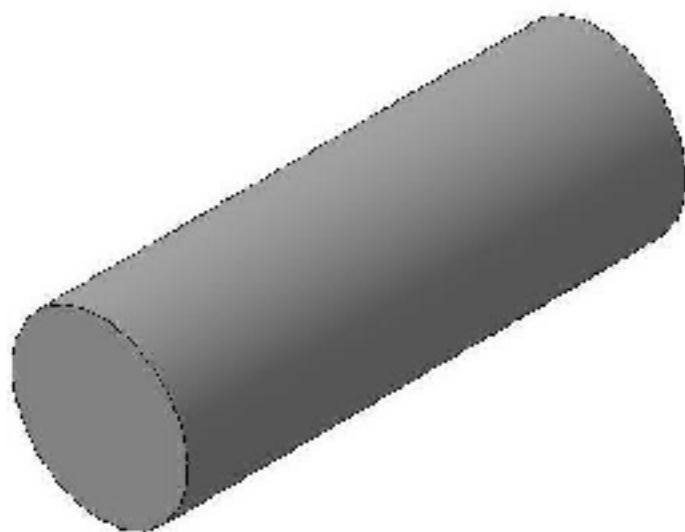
3D-модель заготовки із гарячекатаного прокату
